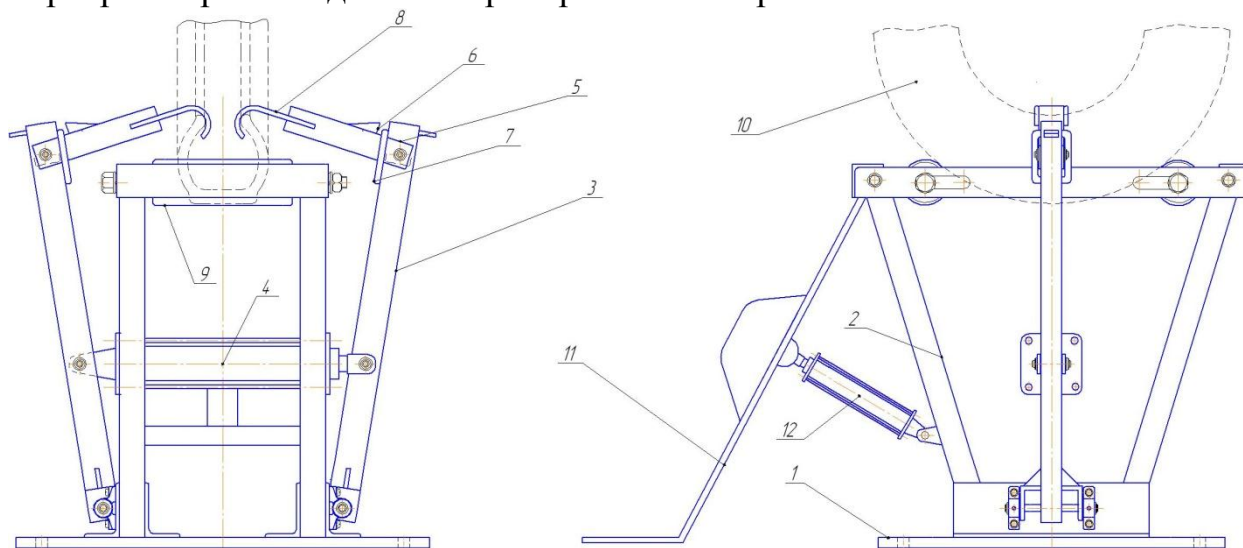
Устройство для осмотра и ремонта пневматических шин:
